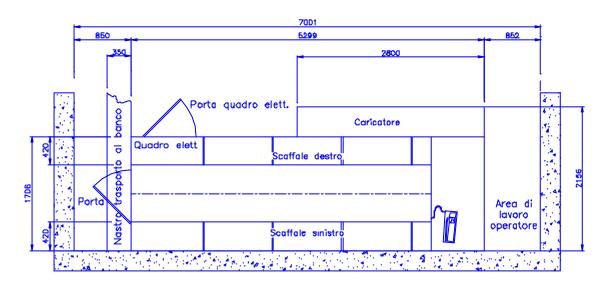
Dimensioni del magazzino a 3 moduli con caricatore
